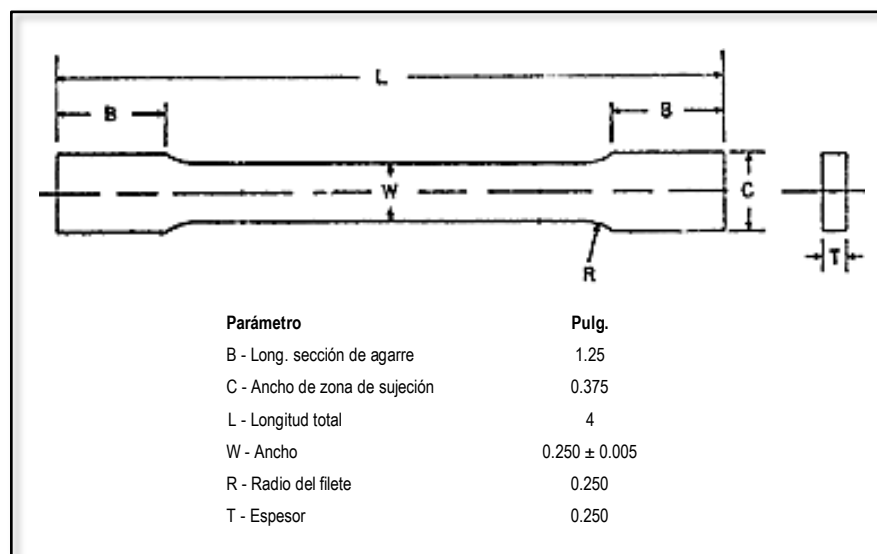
Dimensiones de probeta rectangular de tensión [72].
